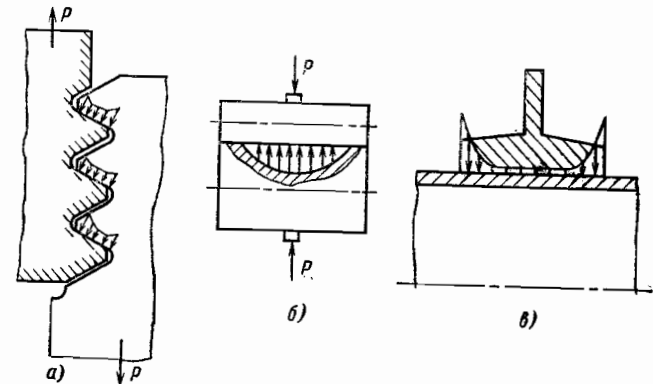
Конструкционные контактные задачи для: а — зубчатого соединения; б — цилиндра конечной длины; в — прессового соединения
